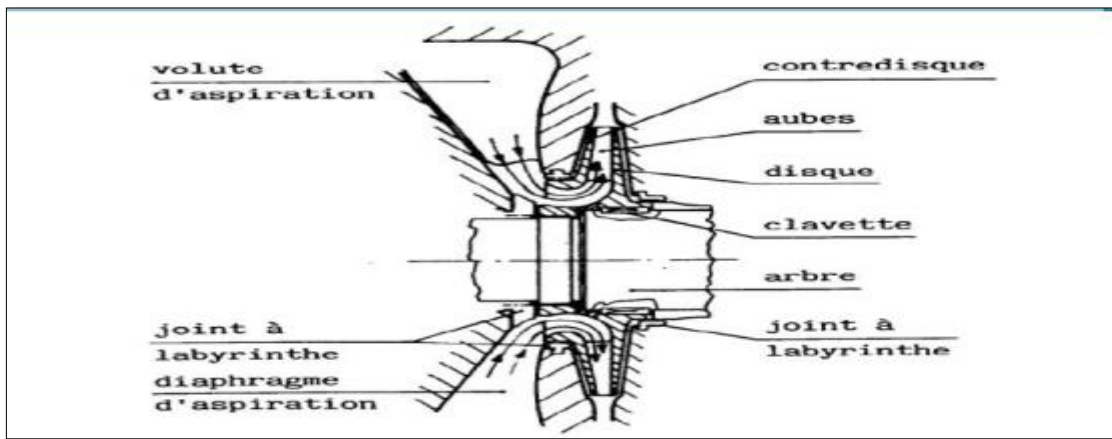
Vue latérale de la roue d'un compresseur centrifuge
